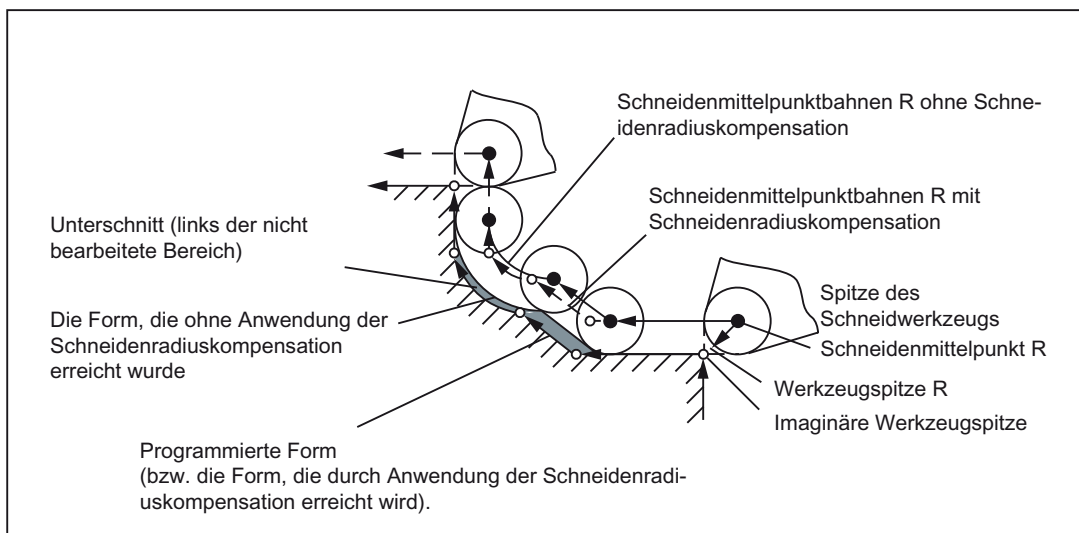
Bearbeitung ohne Schneidenradiuskorrektur
